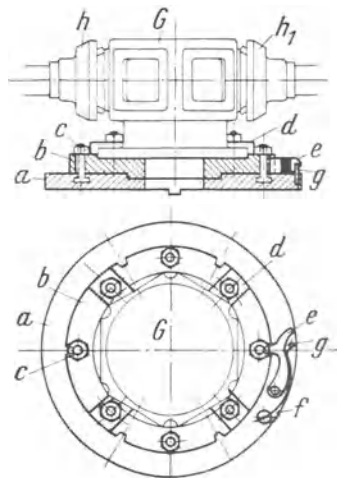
Schwenkvorrichtung zum Fräsen von 6 Flächen an Hauben.
